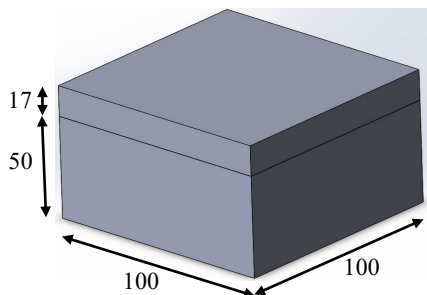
Внешний вид ГК ТС с крышкой без оребрения (модель № 1)
